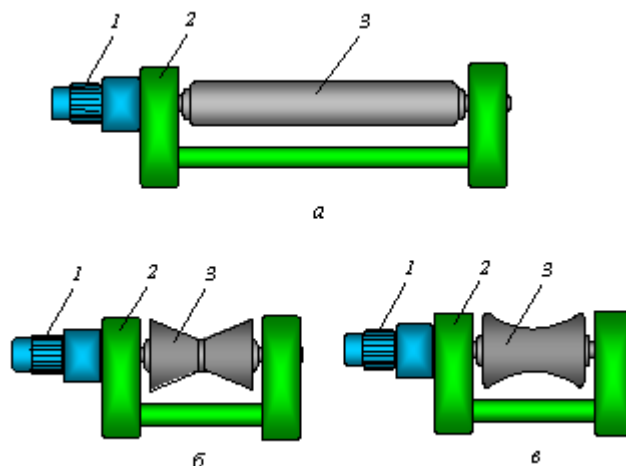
Рольганги с индивидуальным приводом и роликами: *а* — цилиндрическим; *б* — биконическим; *в* — профильным; 1 — мотор-редуктор; 2 — подшипниковая опора; 3 — ролик
